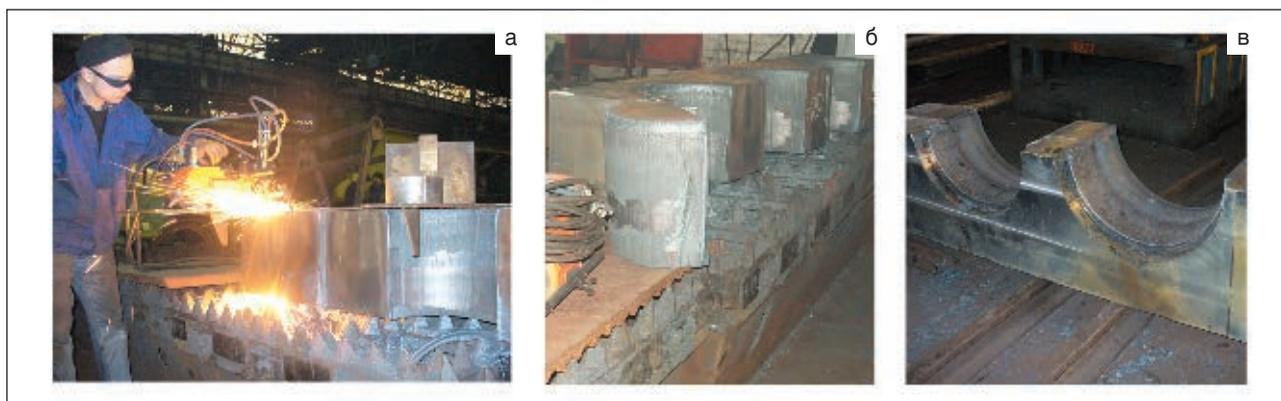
Вырезка отверстий резакм ТОРН-М (а) на заготовках корпуса подшипника из стали 40Х. Поверхность реза заготовки 320 мм, мундштук №1, диаметр режущего канала 3 мм (б). Поверхность реза заготовки 380 мм, мундштук №2, диаметр режущего канала 3,5 мм (в)
